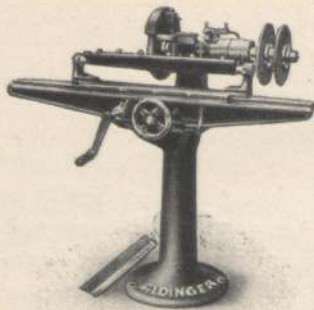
Hobelmesser-Schleifmaschine mit Kehlmesser-Schleifeinrichtung.
